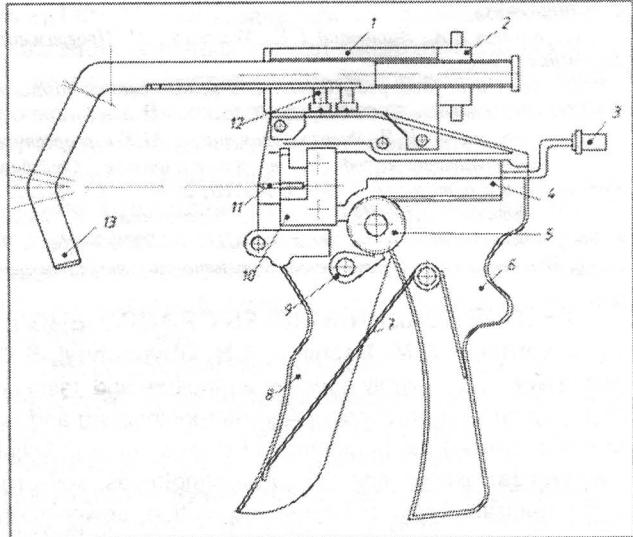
Устройство съема информации индикатора влажности: 1 — направляющая; 2 — гайка; 3 — разъем с — кабелем; 4 — рейка; 5 — шестерня; 6 — корпус; 7 — пружина; 8 — ручка; 9 — собачка; 10 — изолятор; 11 — игла; 12 — винт; 13 — скоба.
